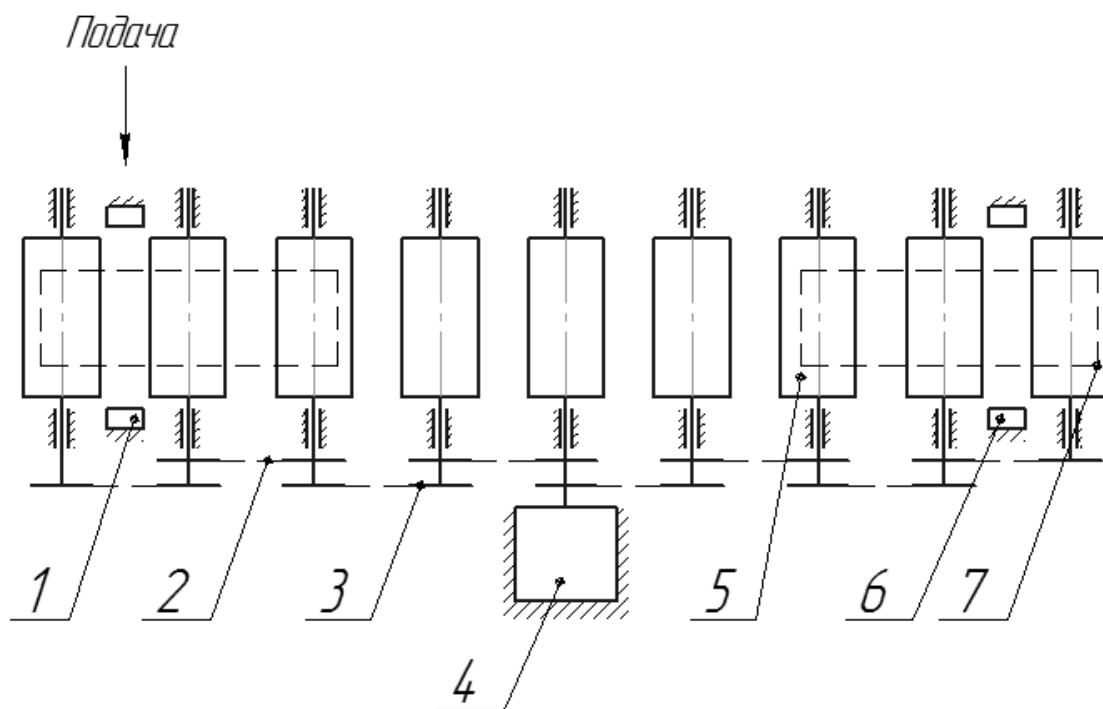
Схема транспортного рольганга (1 – фотодатчик №1; 2 – роликовая цепь; 3 – звездочка; 4 – мотор-редуктор; 5 – ролик; 6 – фотодатчик №2; 7 – заготовка)
